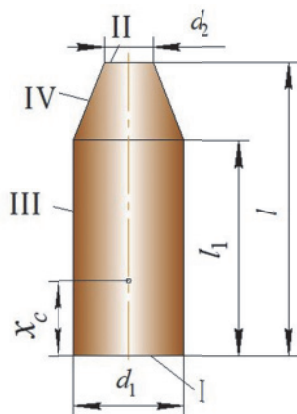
Схема асимметричной заготовки с торцом в форме усеченного конуса с обозначением геометрических параметров и ограничивающих ее поверхностей
